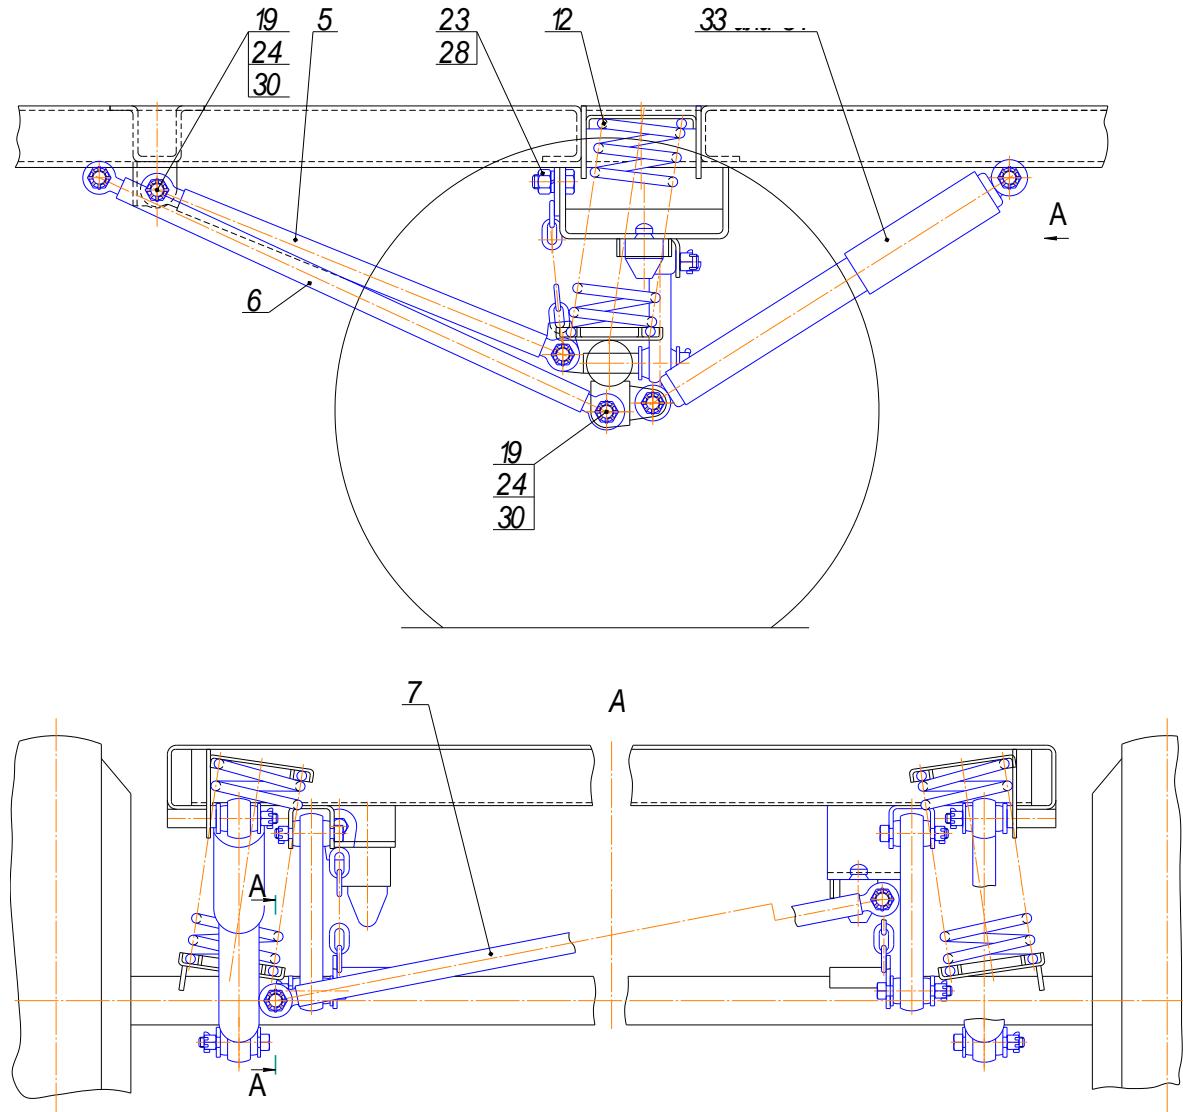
Підвіска причепа «ПГМФ – 8232»
